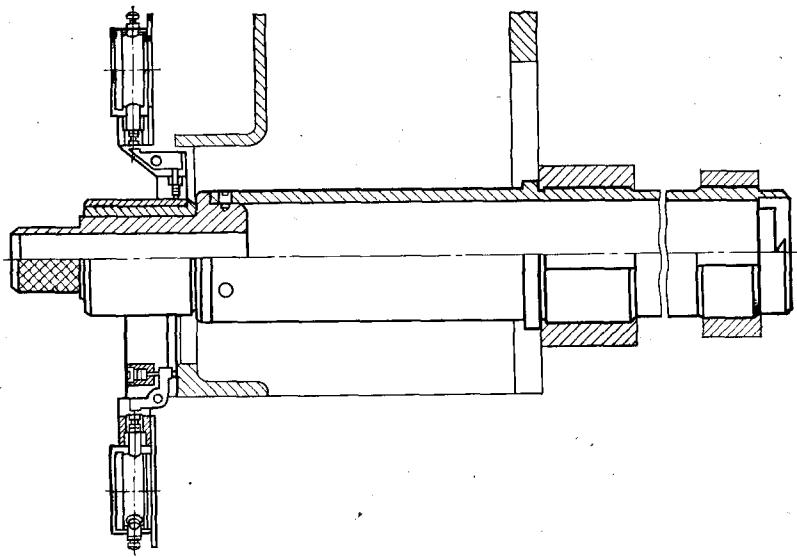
Приспособление для проверки соосности отверстия и перпендикулярности заднего торца картера сцепления оси коленчатого вала
